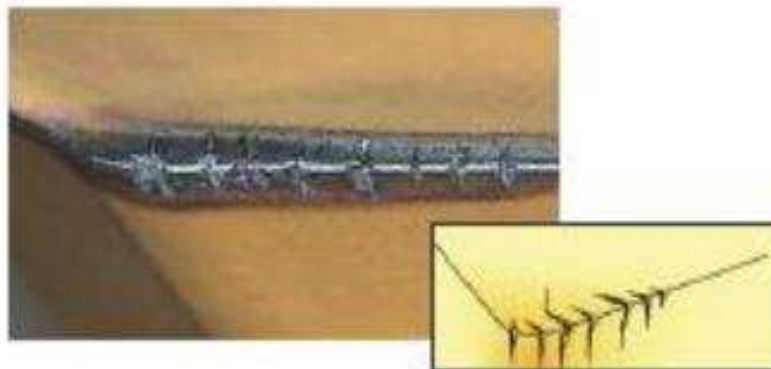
Opotřebení ve tvaru vrubu [10]
